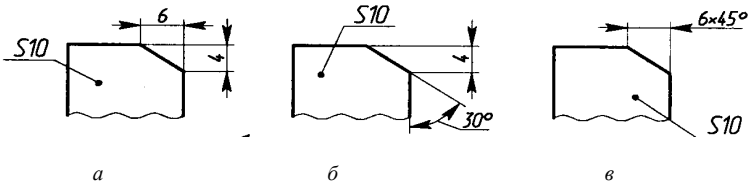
Простановка размеров фасок: *а* – двумя линейными размерами; *б* – одним линейным и угловым размером; *в* – комбинированным способом
